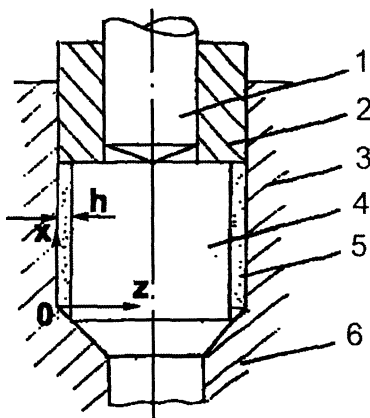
Схема к расчету теплопередачи при горячем выдавливании: 1 – хвостовик; 2 – втулка; 3 – контейнер; 4 – заготовка; 5 – смазка; 6 – матрица
